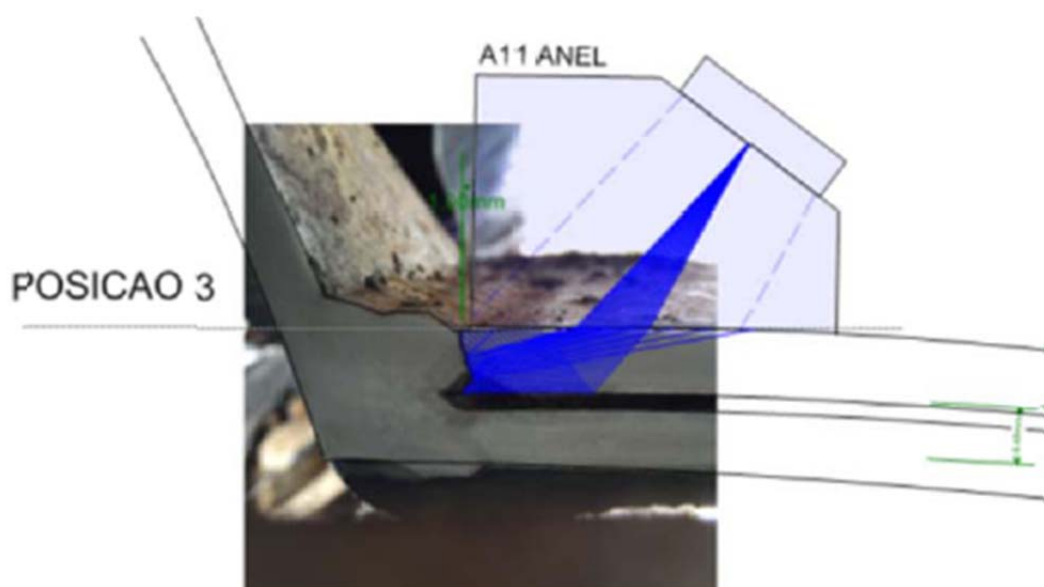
Foto mostrando as limitações para detecção e dimensionamento de trincas na solda, se houvesse uma trinca na margem da solda do pescoço.
